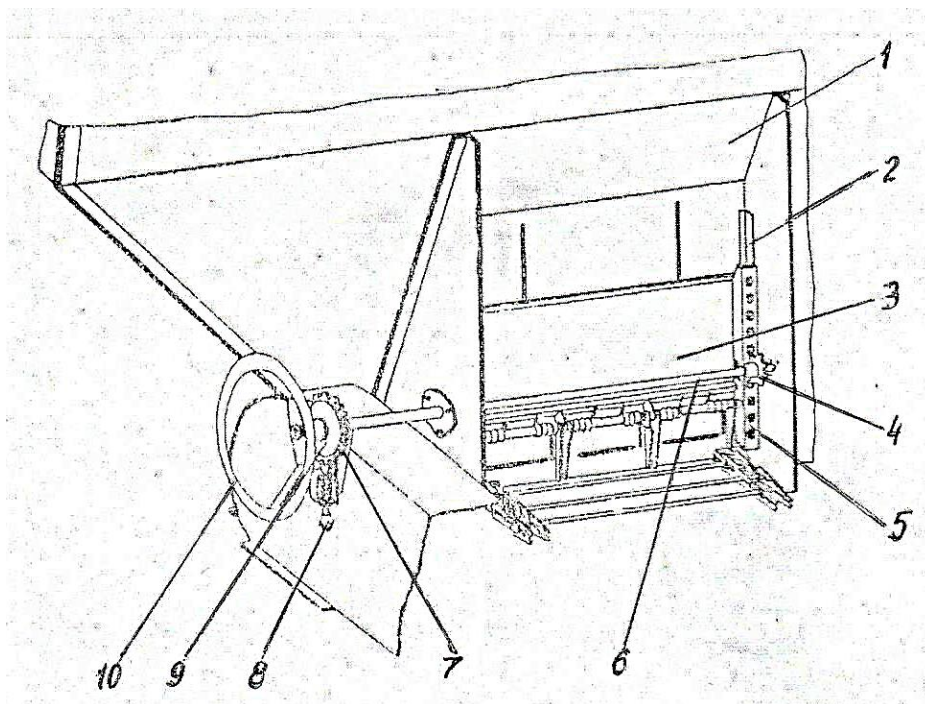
Устройство дозирующее: 1 – задний борт кузова; 2 – направляющая; 3 – дозирующая заслонка; 4 – звездочка; 5 – рейка; 6 – вал; 7 – зубчатое колесо; 8 – фиксатор; 9 – лимб; 10 – штурвал
